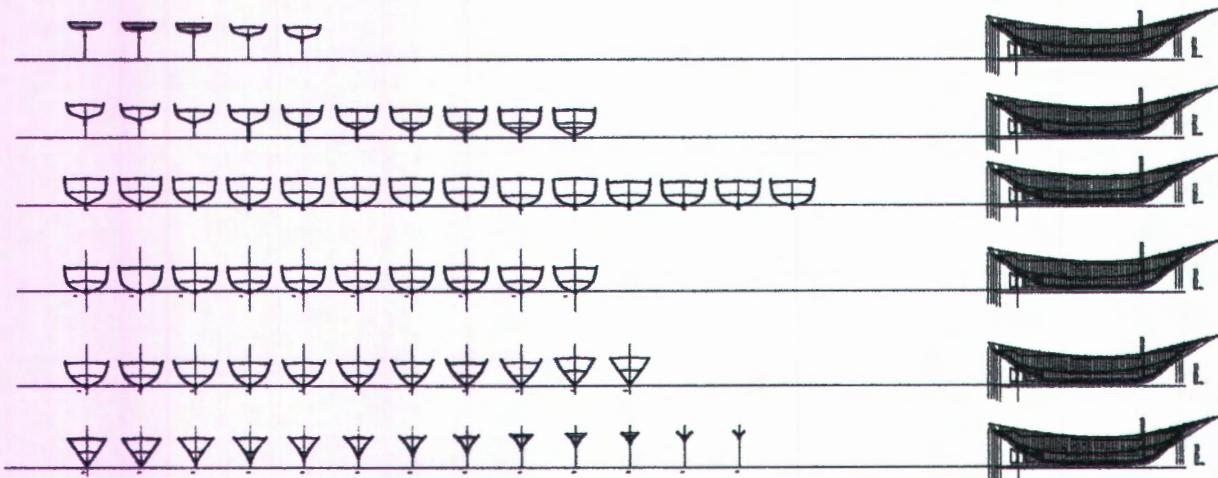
Rencana pelintang konstriksi gading bawah aluminiu
